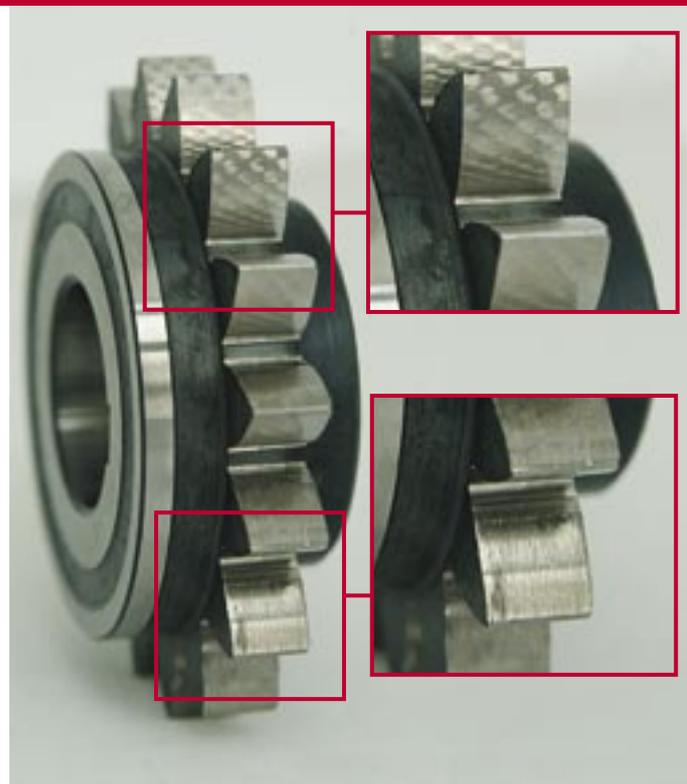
FZG Fresslasttest - ADDINOL Eco Gear
